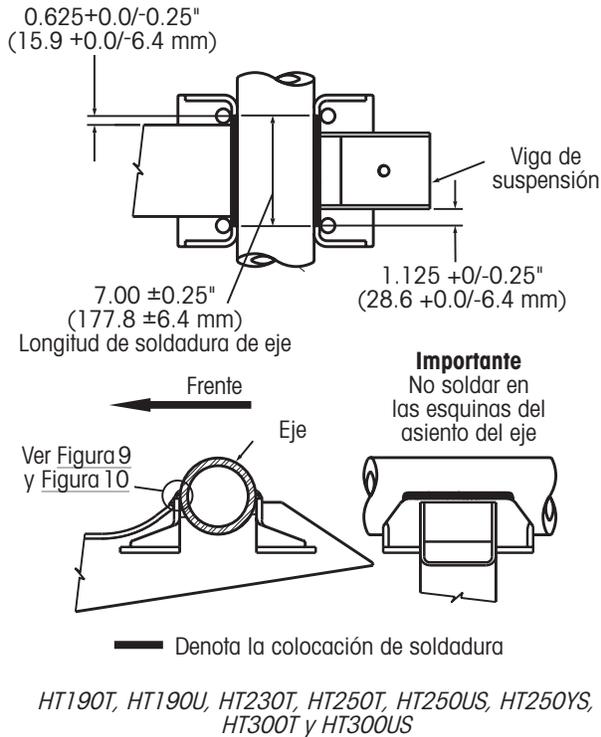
Longitud y posición de cordón de soldadura de eje.
